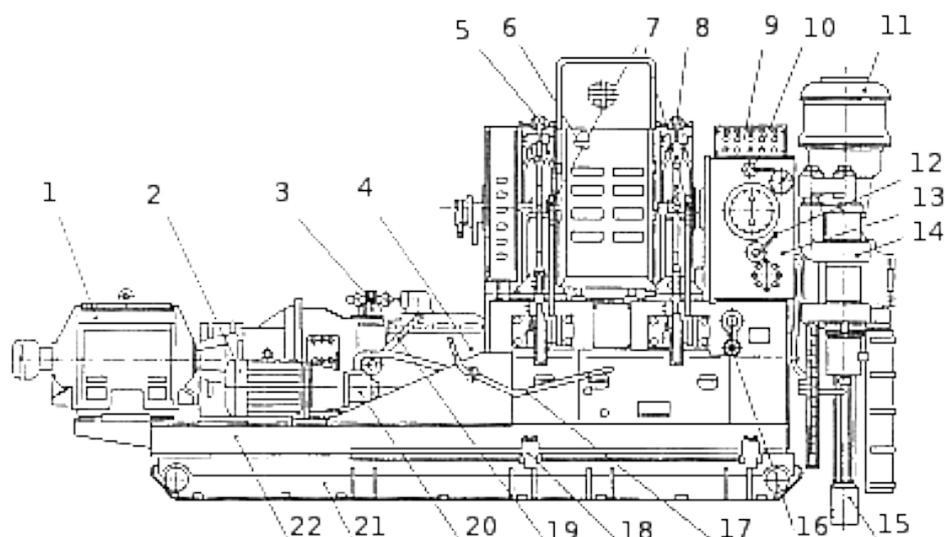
Общий вид бурового станка ЗИФ-1200МРК:
